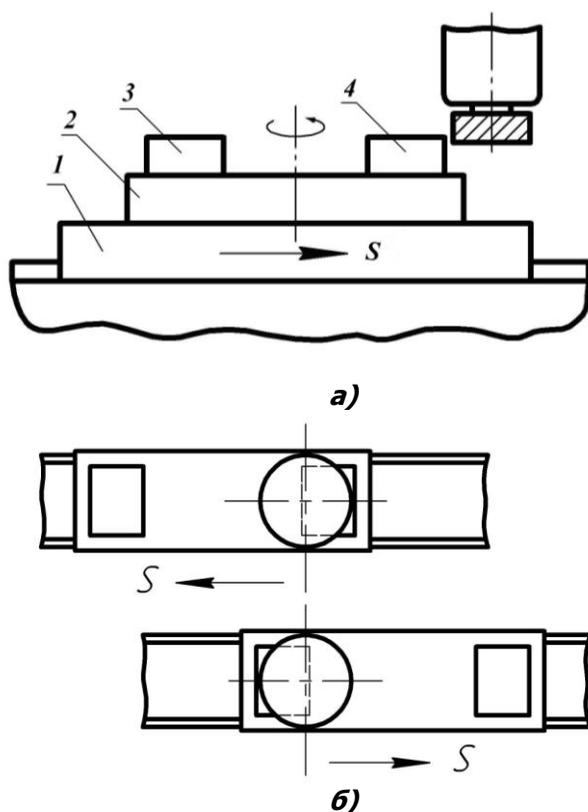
Схема двухпозиционной фрезерной операции на вертикально-фрезерном станке
